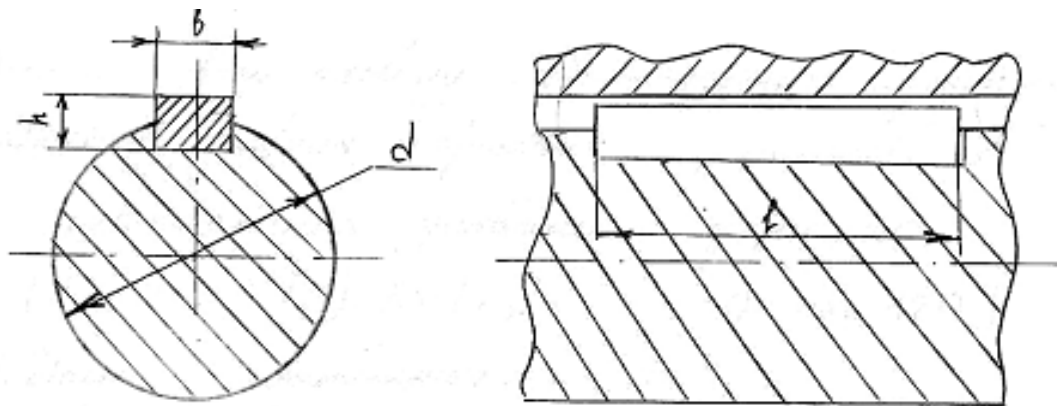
Розрахункова схема шпоночного з'єднання
